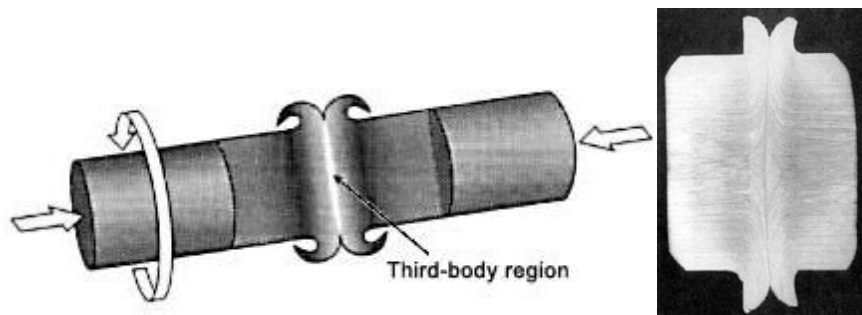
Soldadura por fricción. Izquierda: esquema del proceso [110]. Derecha: macrografía de una sección longitudinal de una soldadura en compuesto [111].
